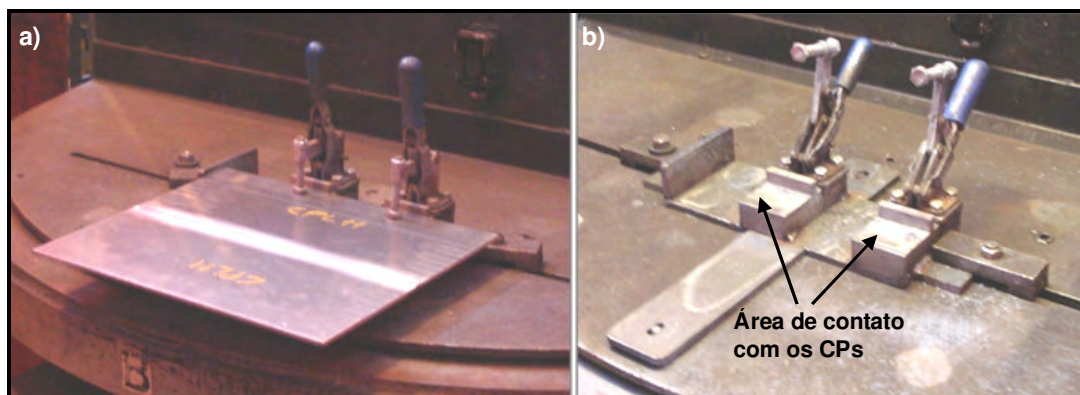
Gabarito de soldagem utilizado: (a) fixado na mesa e com a placa de teste montada; e (b) apenas fixado na mesa.
